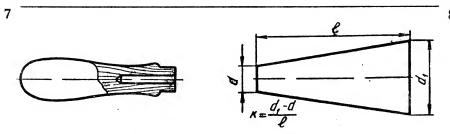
Чертеж ручки к напильнику (местный разрез).
